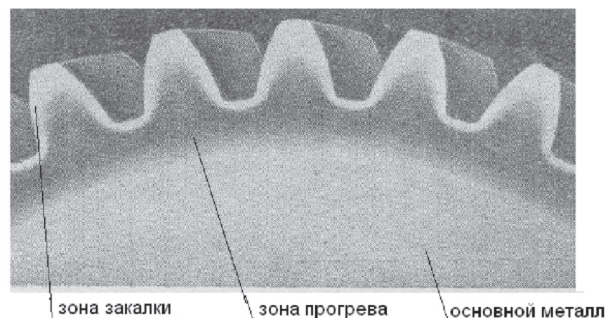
Внешний вид распределения зон нагрева и закалки для зубчатых поверхностей из стали ПП после индукционного поверхностного нагрева
